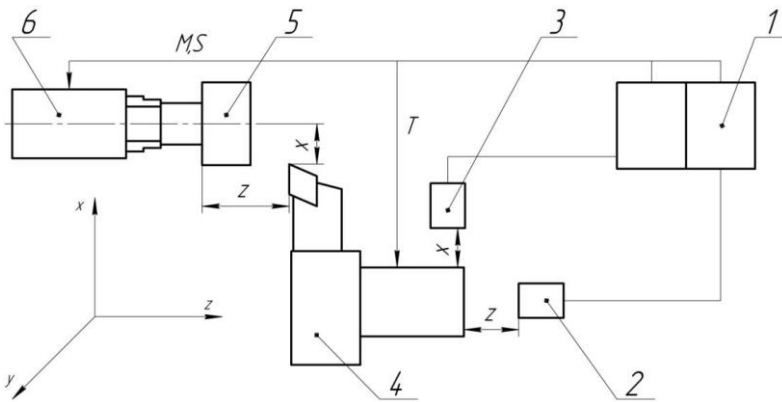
Схема обробки деталі на верстаті з ЧПК (1 – блок керування ЧПУ; 2, 3 – крокові приводи з подовжньою «z» та поперечною «x» подачею; 4 – різцетримач; 5 – заготовка; 6 – безступінчаста коробка швидкостей; M,S – допоміжна функція та команда головного руху; T – команда на зміну інструмента)
